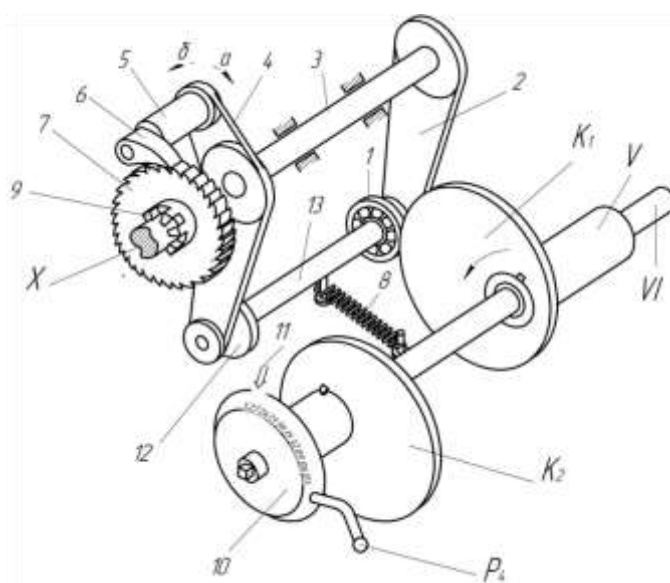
Полуконструктивная схема храпового механизма поперечной подачи
